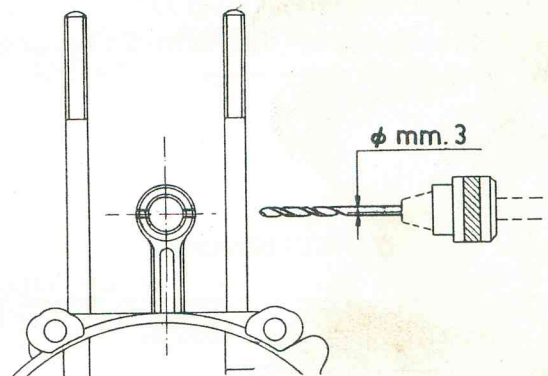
Ausführung der Bohrungen für Schmiermittelzufuhr auf den Pleuelkopf.
